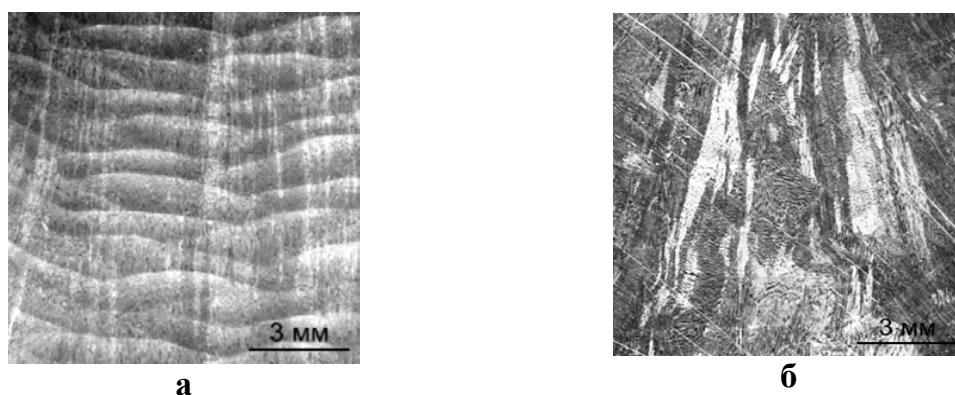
Макроструктура наплавленного металла в поперечном сечении: а – наплавка Плазма-МИГ, б – плазменная наплавка
